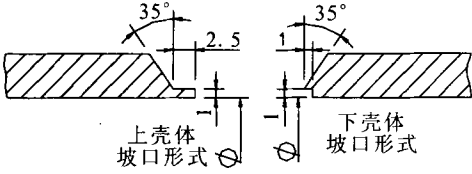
1Cr11Ni2W2MoV 材料壳体焊接结构 2 示意图
